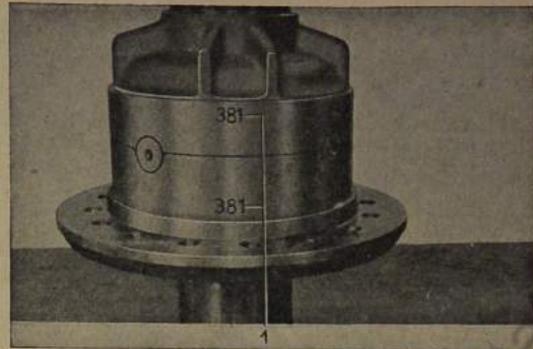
Ausgleichgehäusehälfte zusammenschrauben
